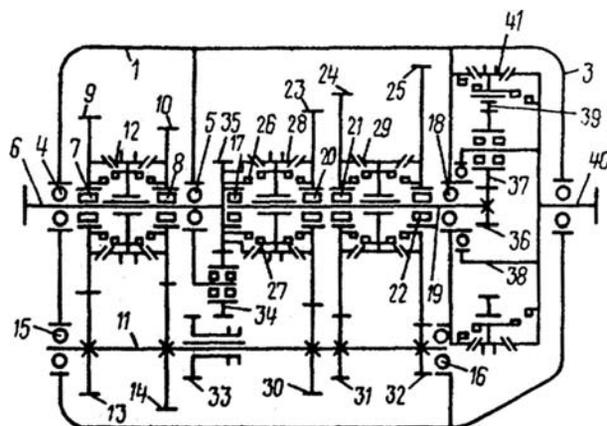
Многоступенчатая коробка передач с делителем и диапазонным редуктором [30], обладающая повышенными КПД и числом передач заднего хода
